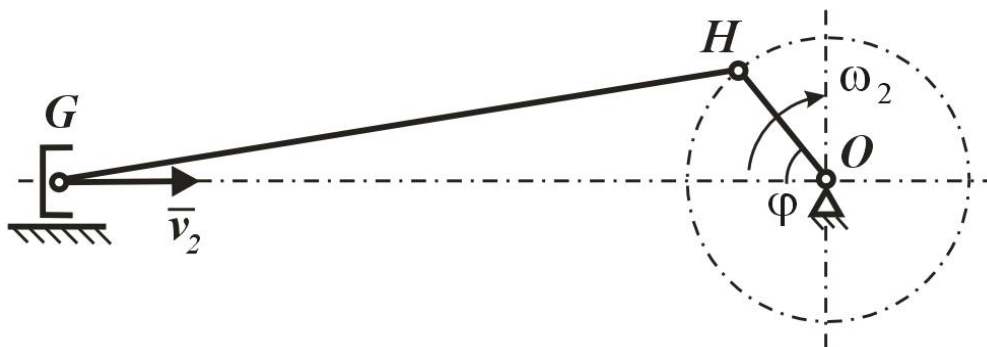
Кинематическая схема возвратно-поступательного движения наплавочной горелки
